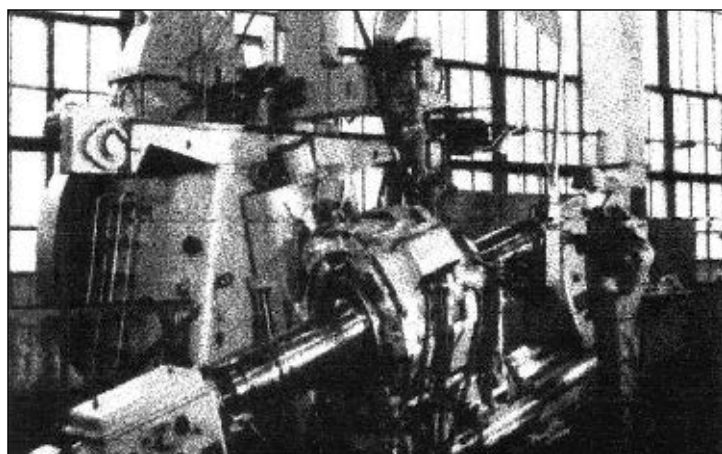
Наплавка валка сортопрокатного стана на вальценаплавочном станке КЖ–9711
